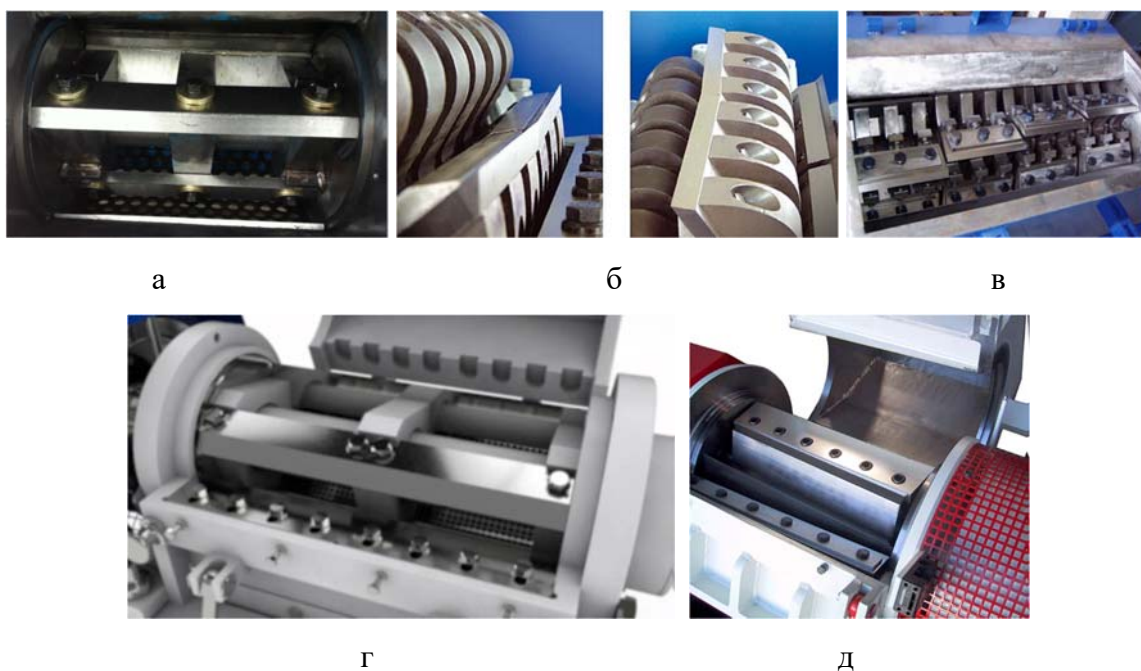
Конструктивно-технологические особенности рабочих органов роторных дробилок: а – прямой рез; б – *V*-образный рез; в – сегментный рез; г – косой рез; д – ножничный рез
